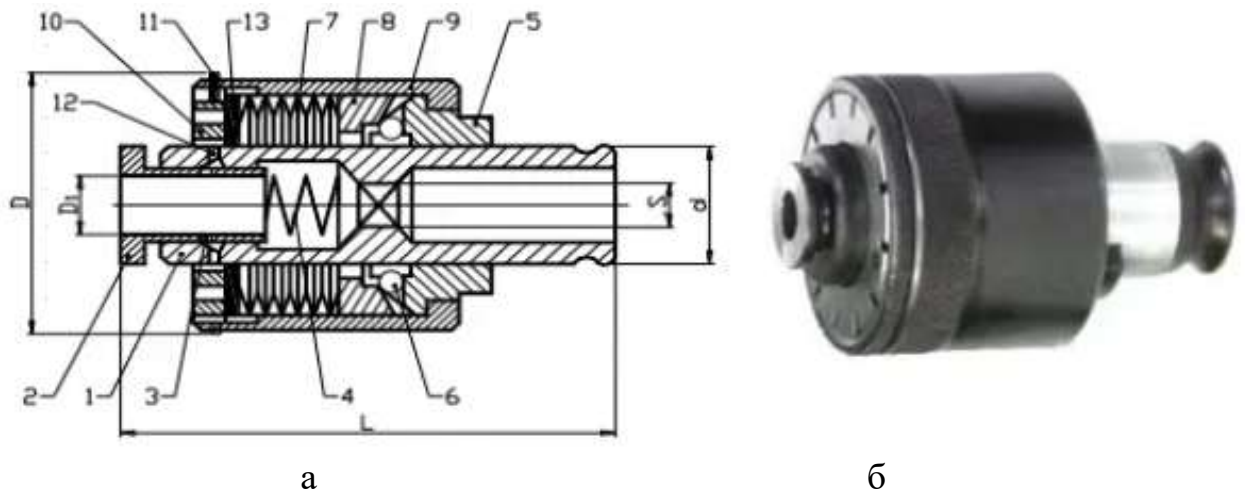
Схем та конструкція запобіжної головки для мітчиків
